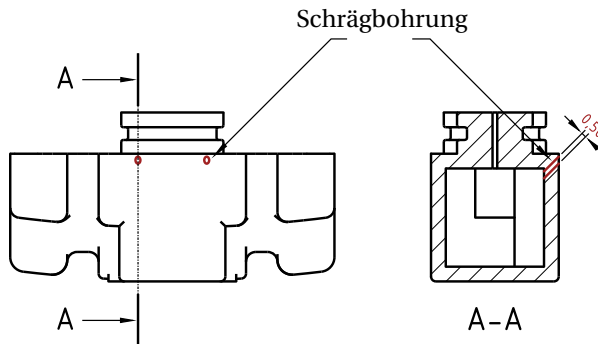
Technische Zeichnung des Unterteils mit in Rot hervorgehobenen Schrägbohrungen
